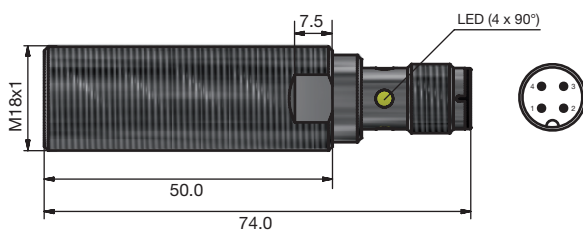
Lange Ausführung, bündiger Einbau, Steckversion
